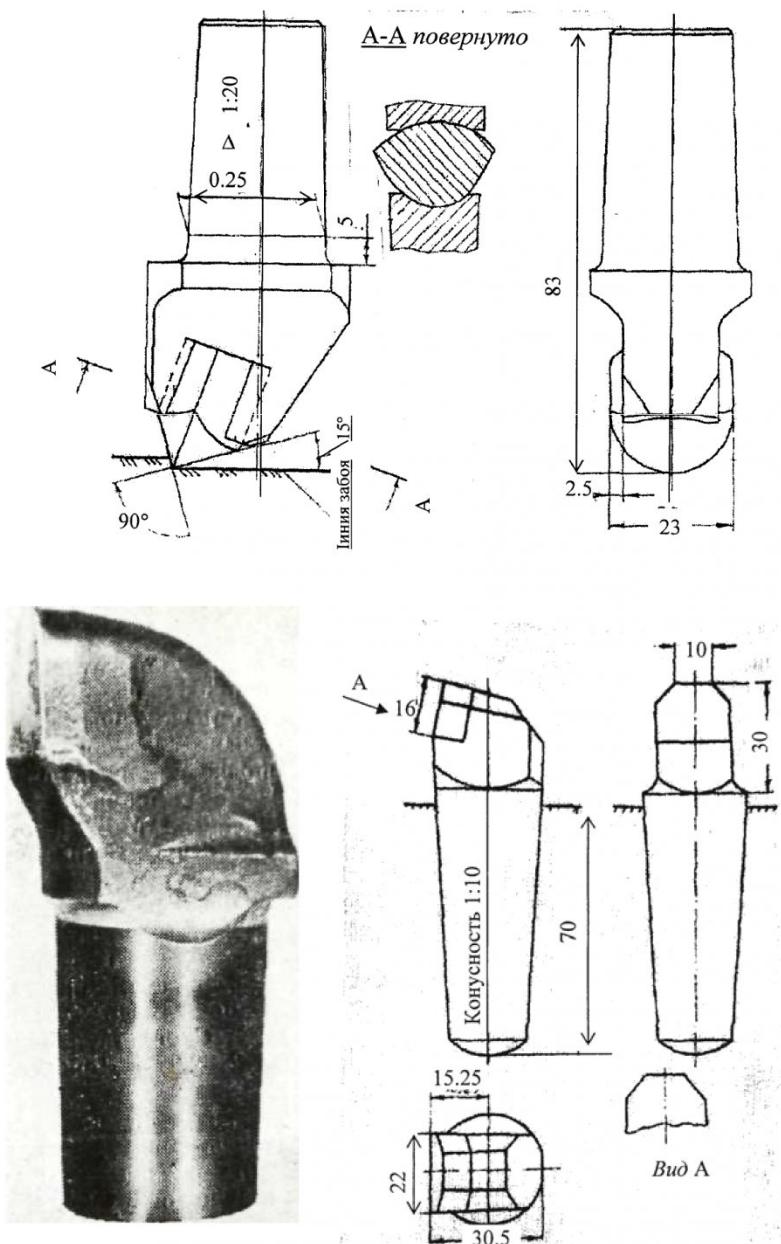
Резцы с усиленными державками и твердосплавными пластинами для оснащения режущих буровых долот:
